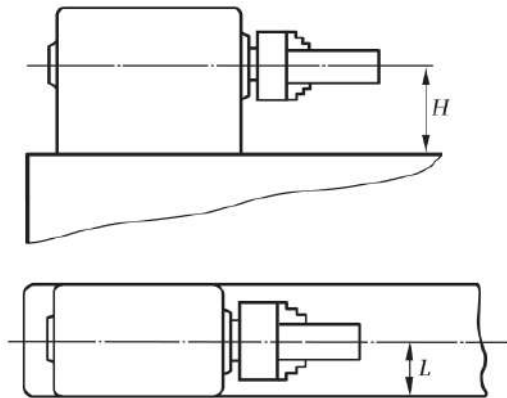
Розміри токарного верстата, що змінюються внаслідок нагрівання переднього підшипника передньої бабки
